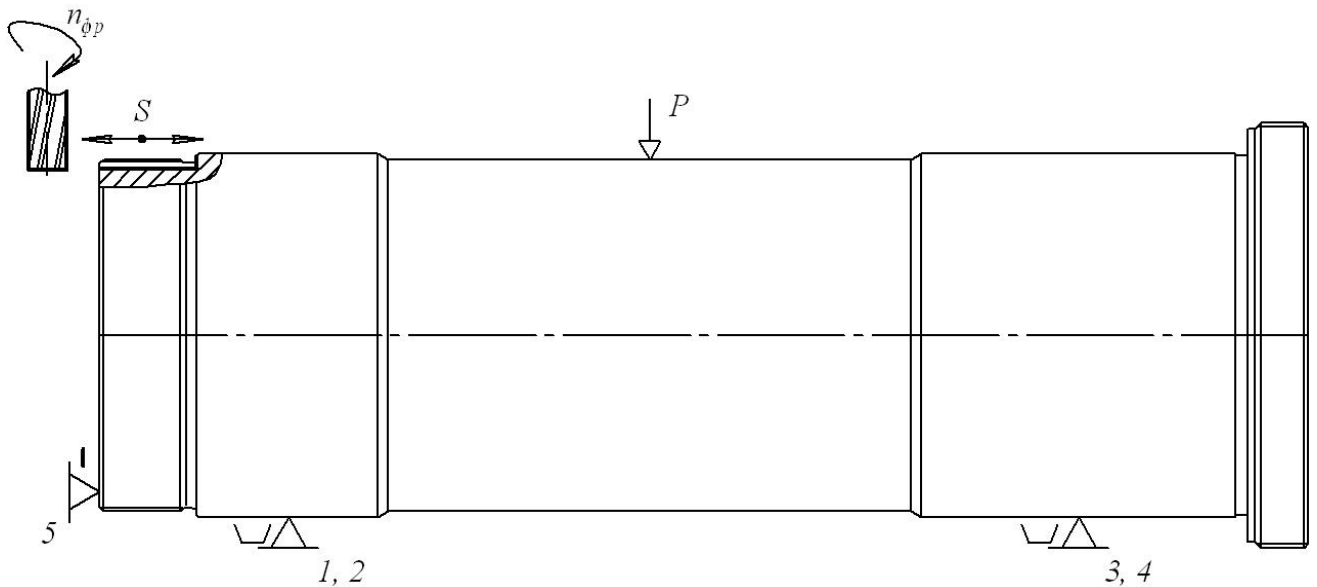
Схема закріплення заготовки при фрезеруванні паза
